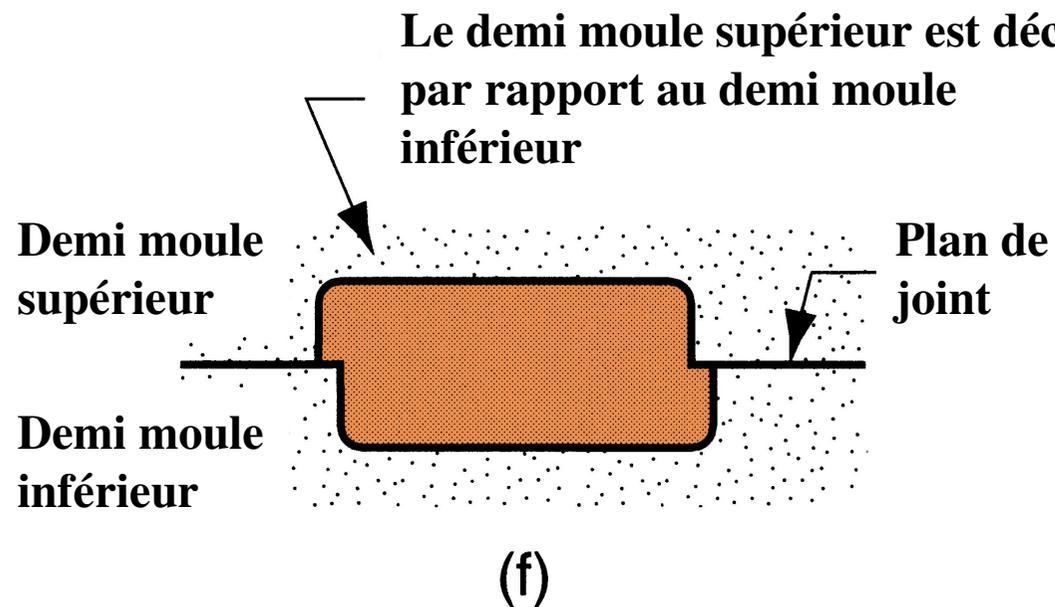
Défaut de moulage en sable : (f) défaut de joint
